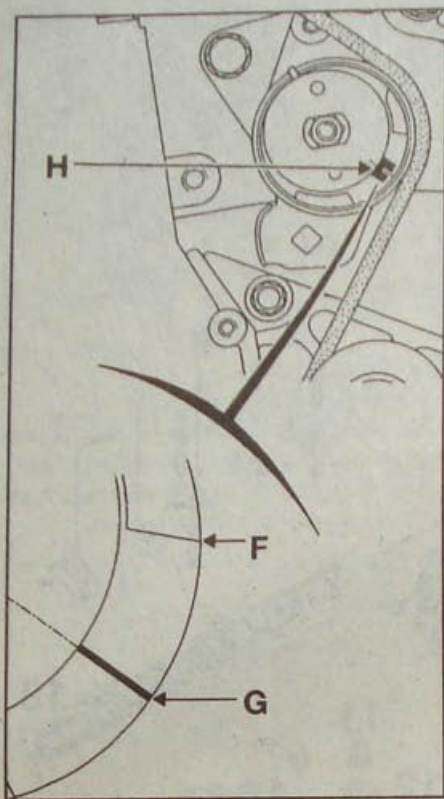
Расположение меток при натяжении ремня привода газораспределительного механизма:
